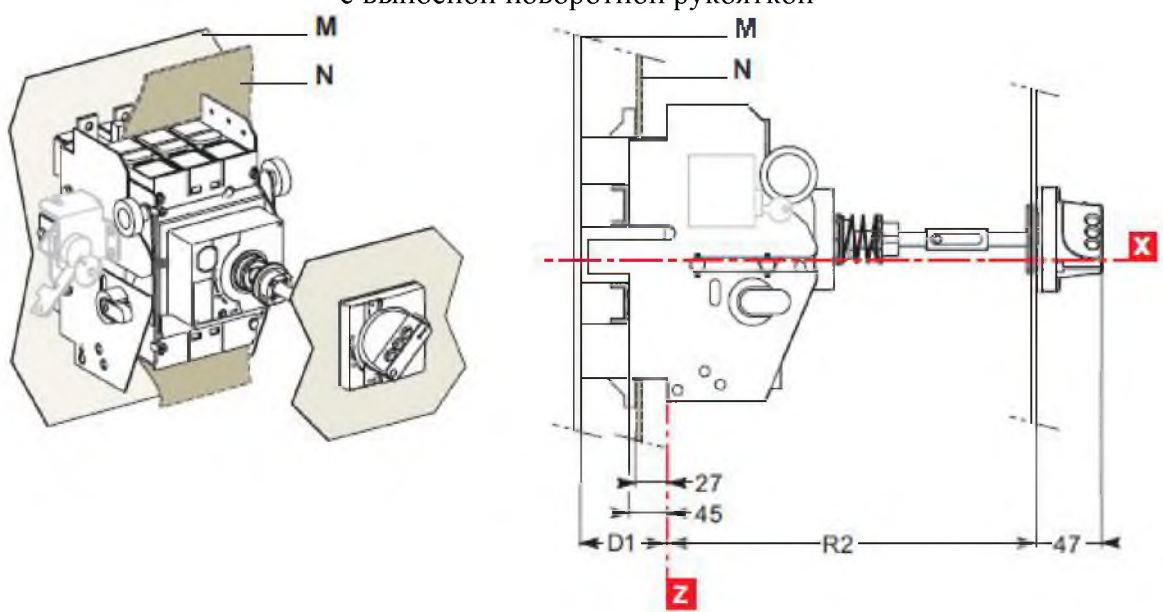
Габаритные размеры выкатного автоматического выключателя ВА-СЭЩ-МС с выносной поворотной рукояткой
